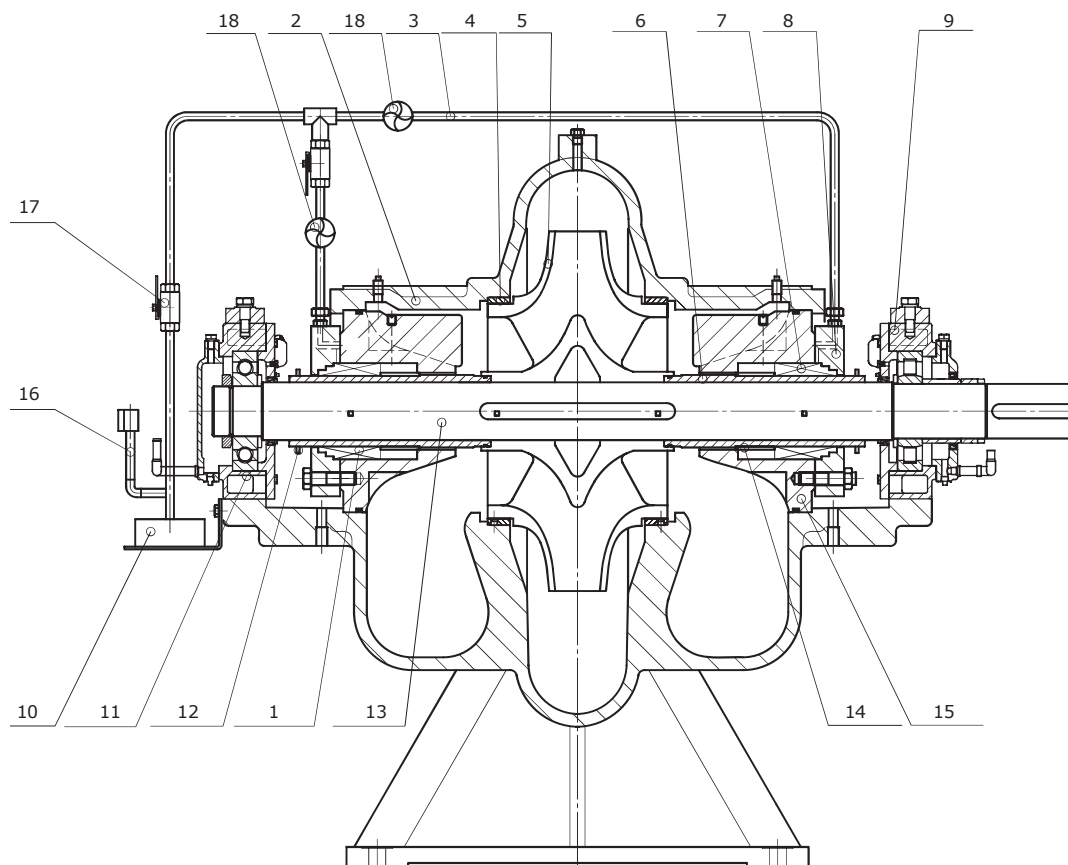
Вид в разрезе, стандартный тип исполнения 5
